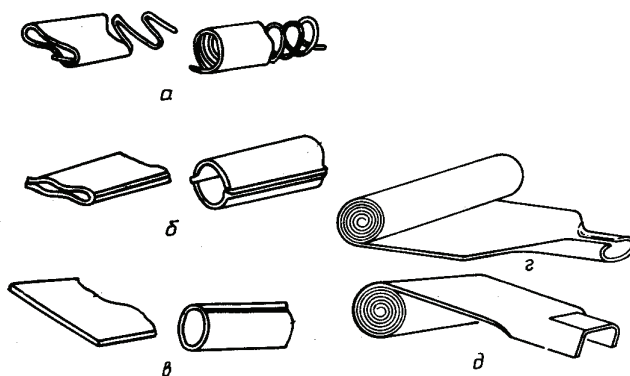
Схемы формирования трубы или профиля с помощью проволоки или каркаса из сплава с памятью (а) и из упаковки пакетного типа, включающей две заготовки (б), листовой заготовки (в), рулонной упаковки (г, д).
